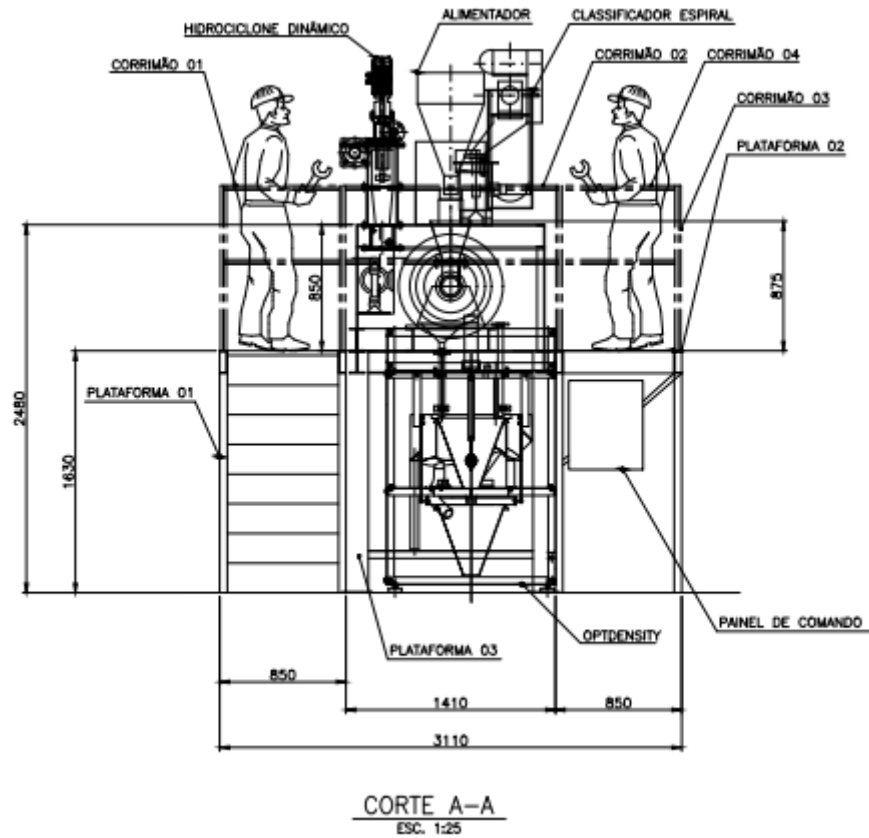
Corte A-A do Desenho da Planta Piloto.
